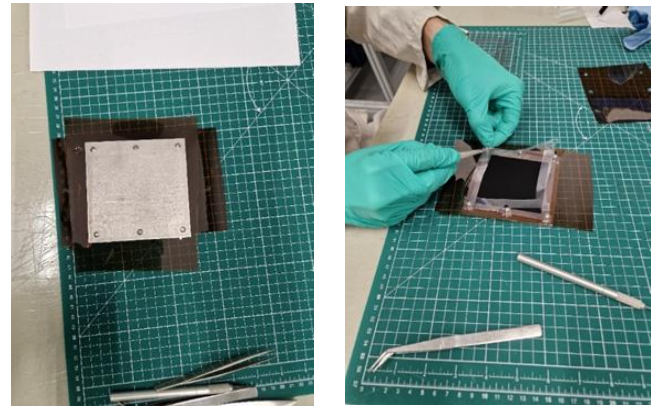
Positionnement des sous-joints (a) et découpe d'un sous-joint à l'aide d'un emporte-pièce et sous presse (b)
